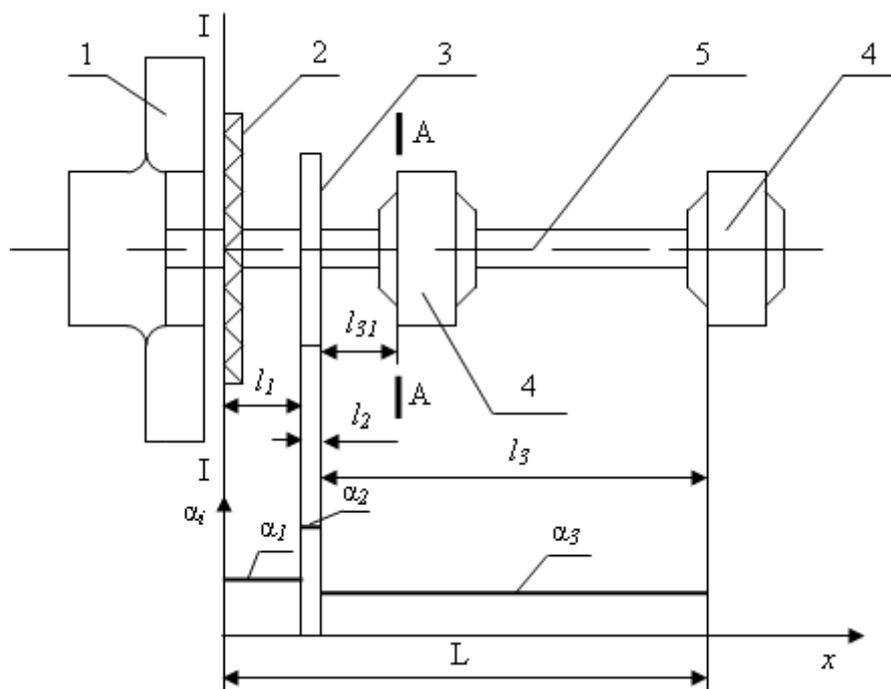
Расчётная схема опорного вала вентилятора для дымоудаления 1-рабочее колесо; 2-тепловой экран; 3- теплоотводящее устройство; 4- опорный подшипник; 5- промежуточный вал
